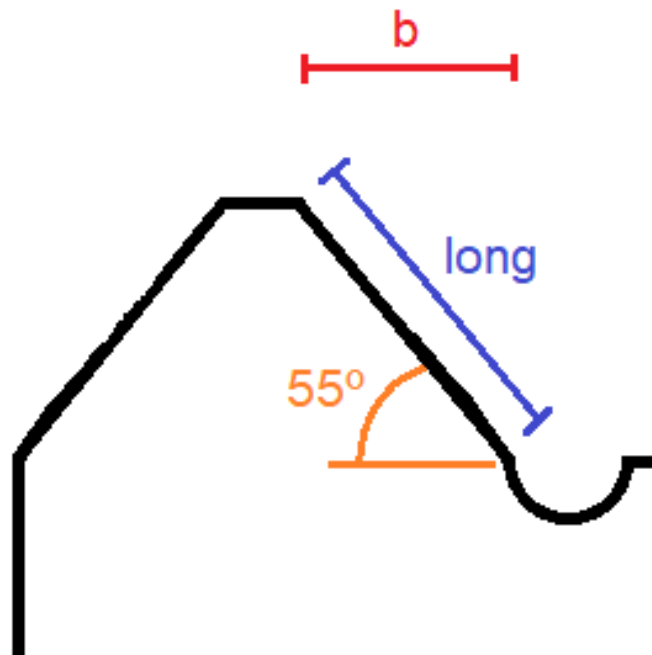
Dimensiones a emplear en el cálculo de la longitud del flanco de la guía prismática.
